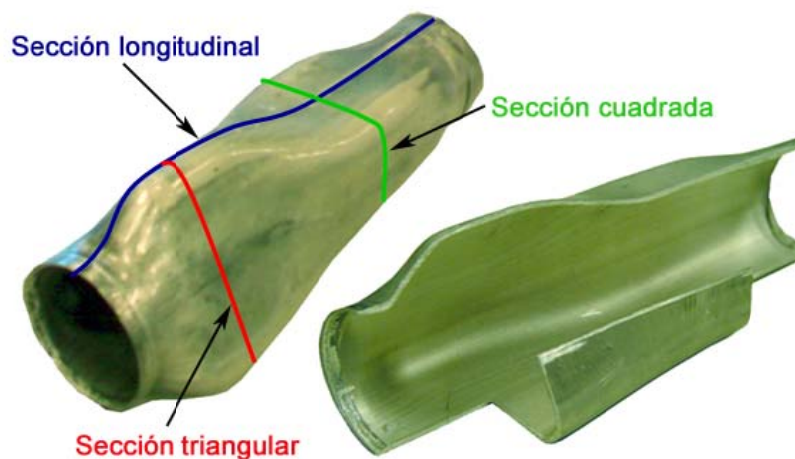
Secciones de control definidas para la verificación de la pieza
